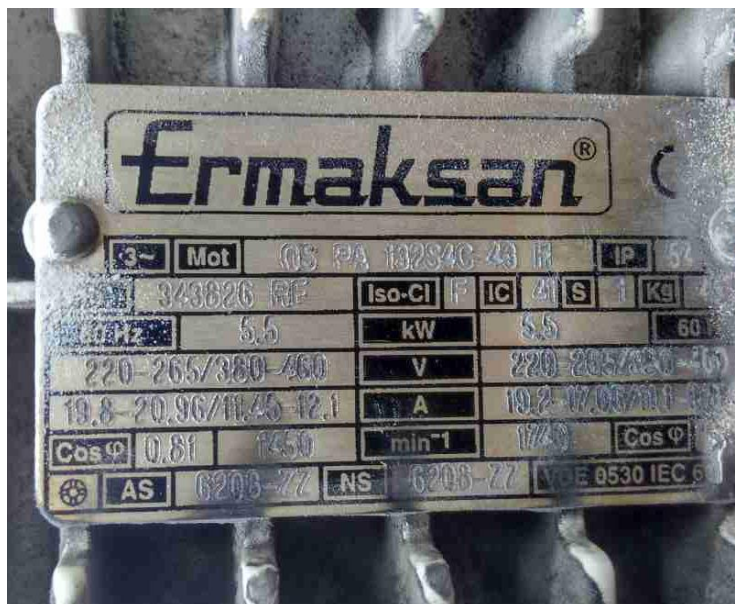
Placa de características técnicas del motor de la dobladora Ermak CNC HAP 1235
